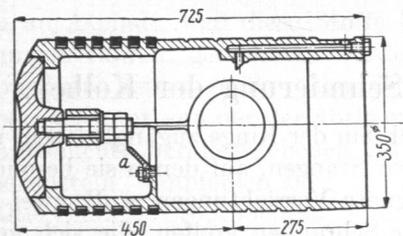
Gasmaschinenkolben mit besonders eingesetztem Boden.
